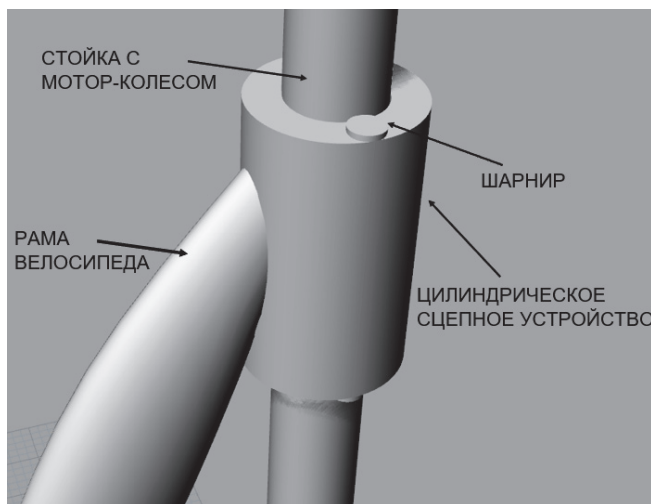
Цилиндрическое сцепное устройство втулочного типа
